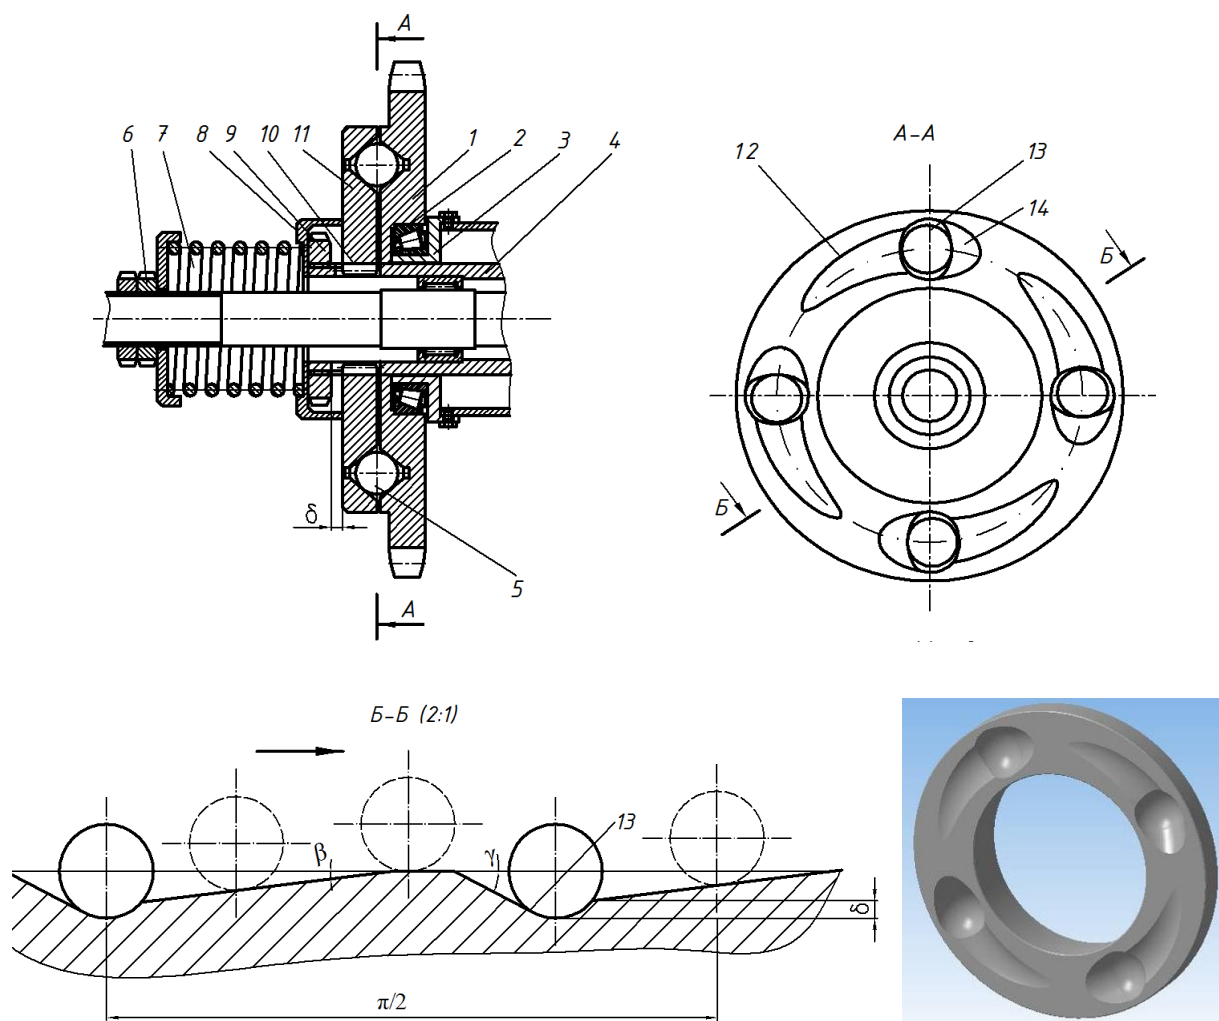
Конструктивна схема запобіжної муфти та загальний вигляд робочої поверхні ведучої півмуфти
